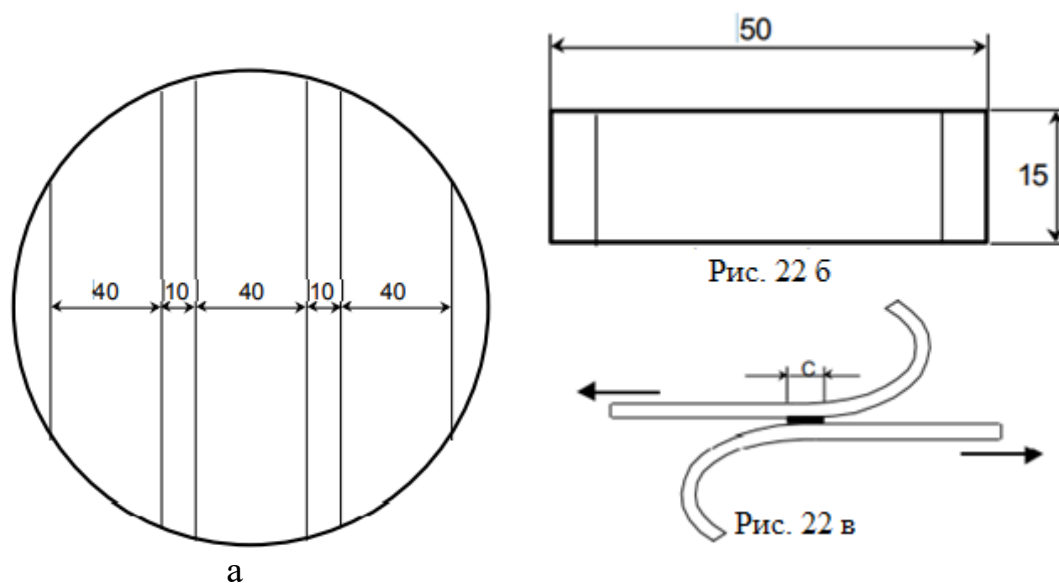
а – расположение нитей на отливке для определения межволоконных сил связи; б – вид образца с нитями; в – принцип проведения испытания
